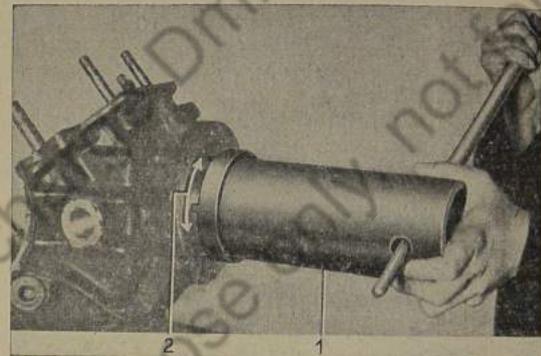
Einstellbuchse für Antriebskegelrad herausschrauben
